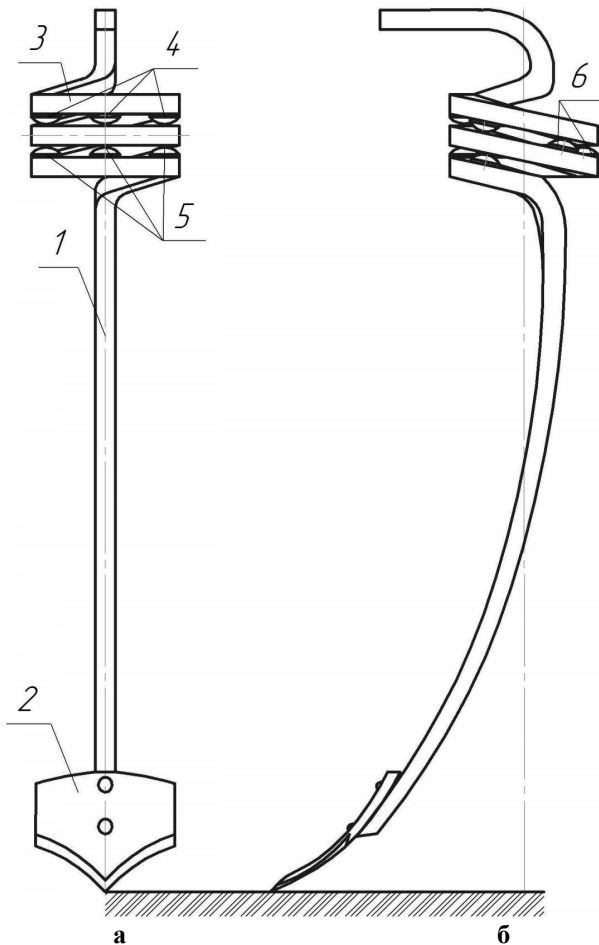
Общий вид рабочего органа культиватора: а) вид спереди; б) вид сбоку.
